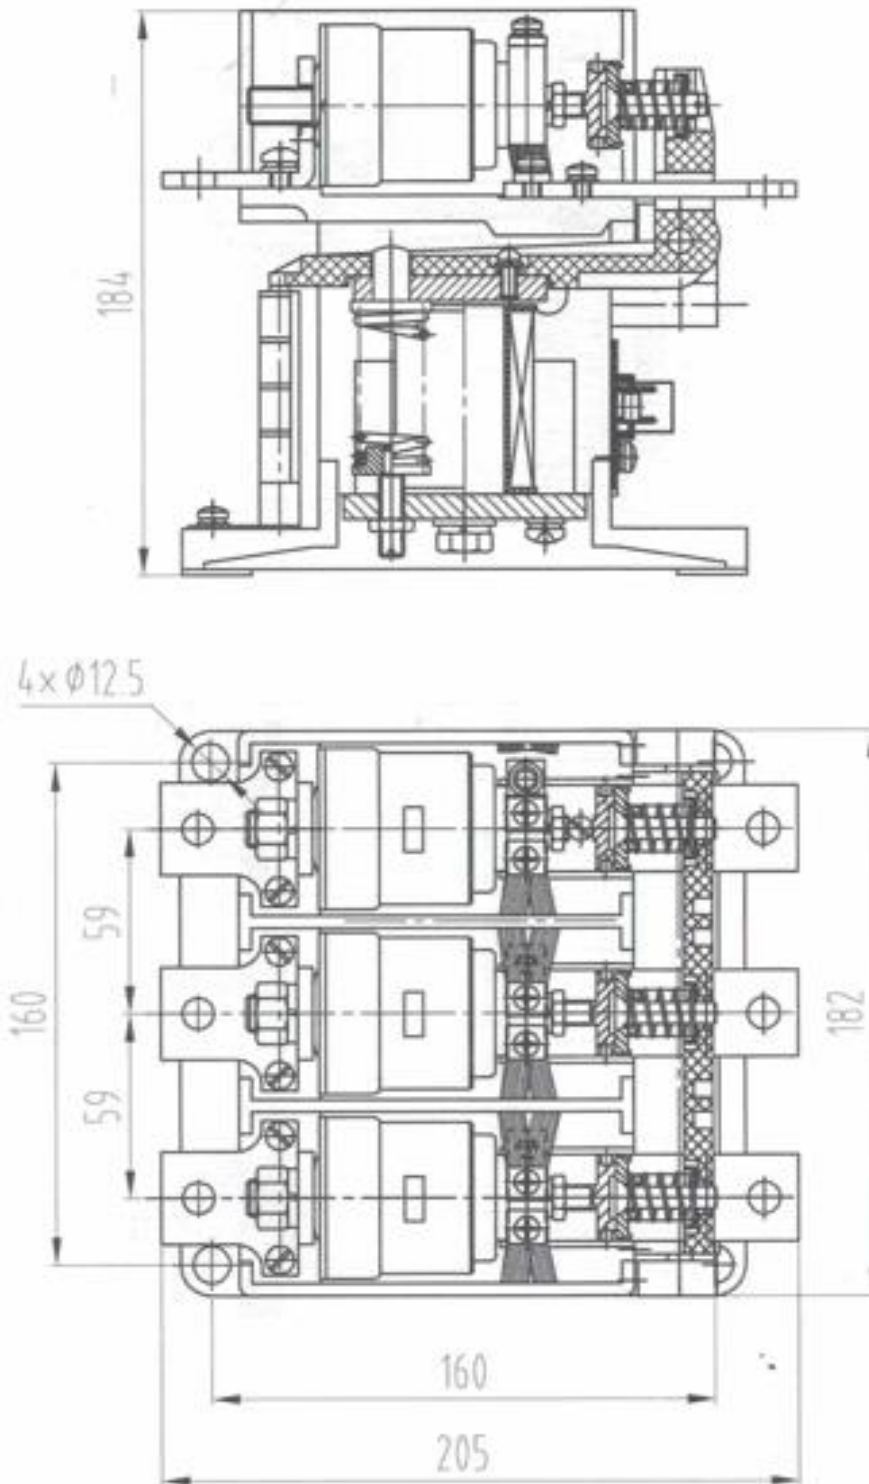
SOSKJ5-80~125~160/1140 desenho e dimensional de instalação
